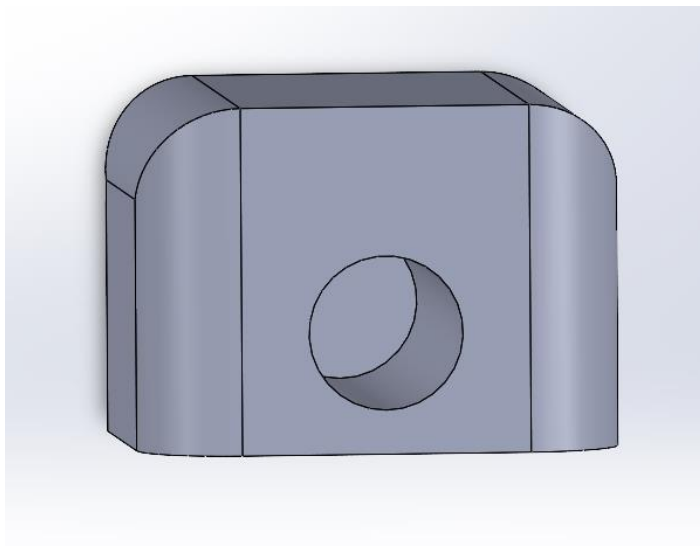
Widok po skosie obrazujący element mechanizmu śrubowo-tocznego – nakrętki.
